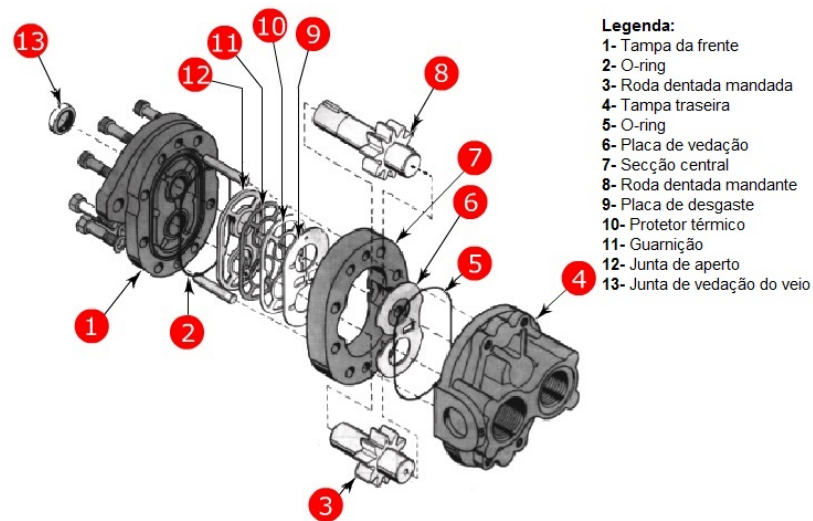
Vista explodida de um bomba de engrenagens exteriores. Adaptado de [7].
